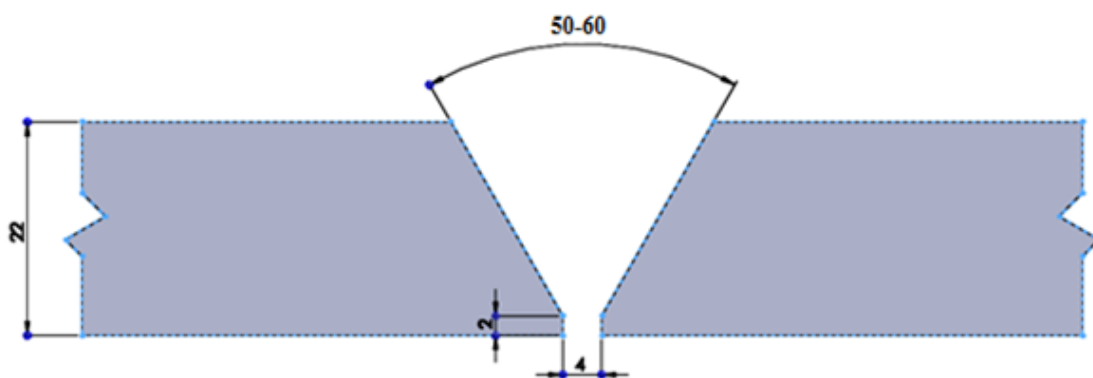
Dimensões em milímetros da junta a soldar.
